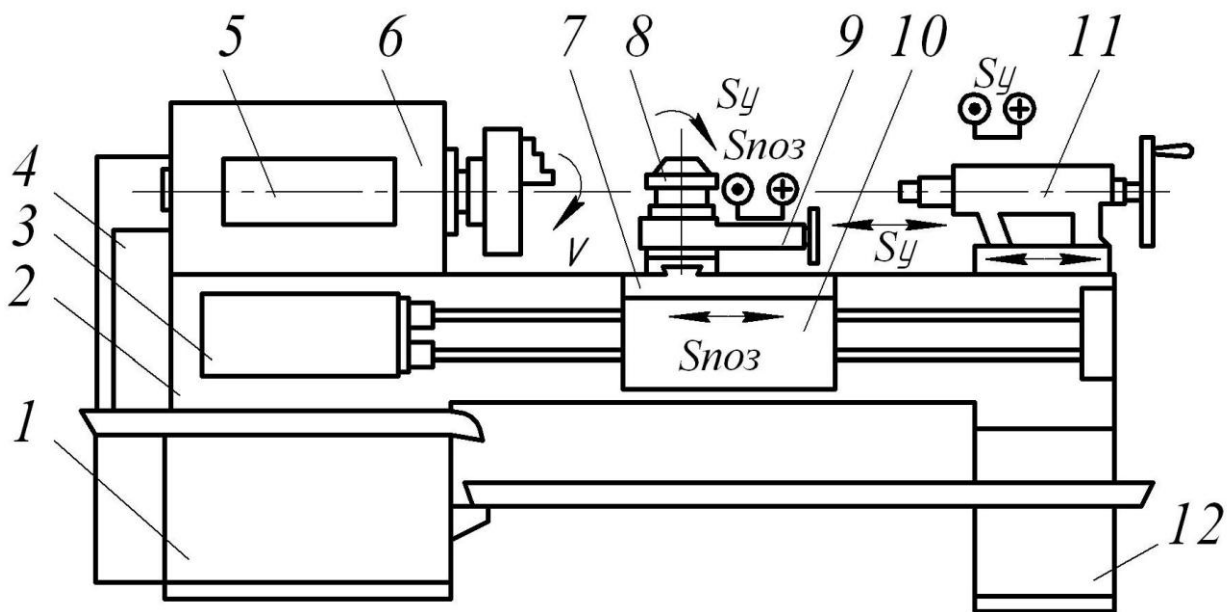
Загальний вигляд токарно-гвинторізного верстата
